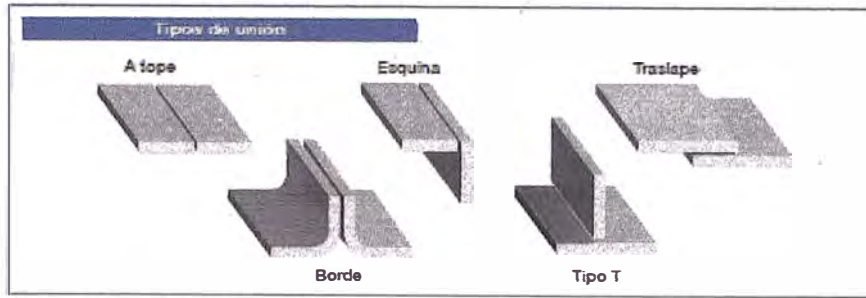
Tipos de uniones en soldadura (Fuente: Manual de Soldadura Indura)
